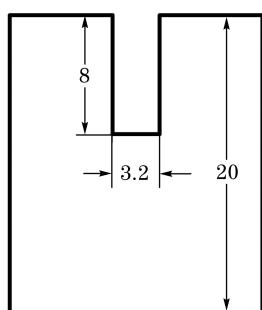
TC4 窄间隙激光焊接坡口尺寸
